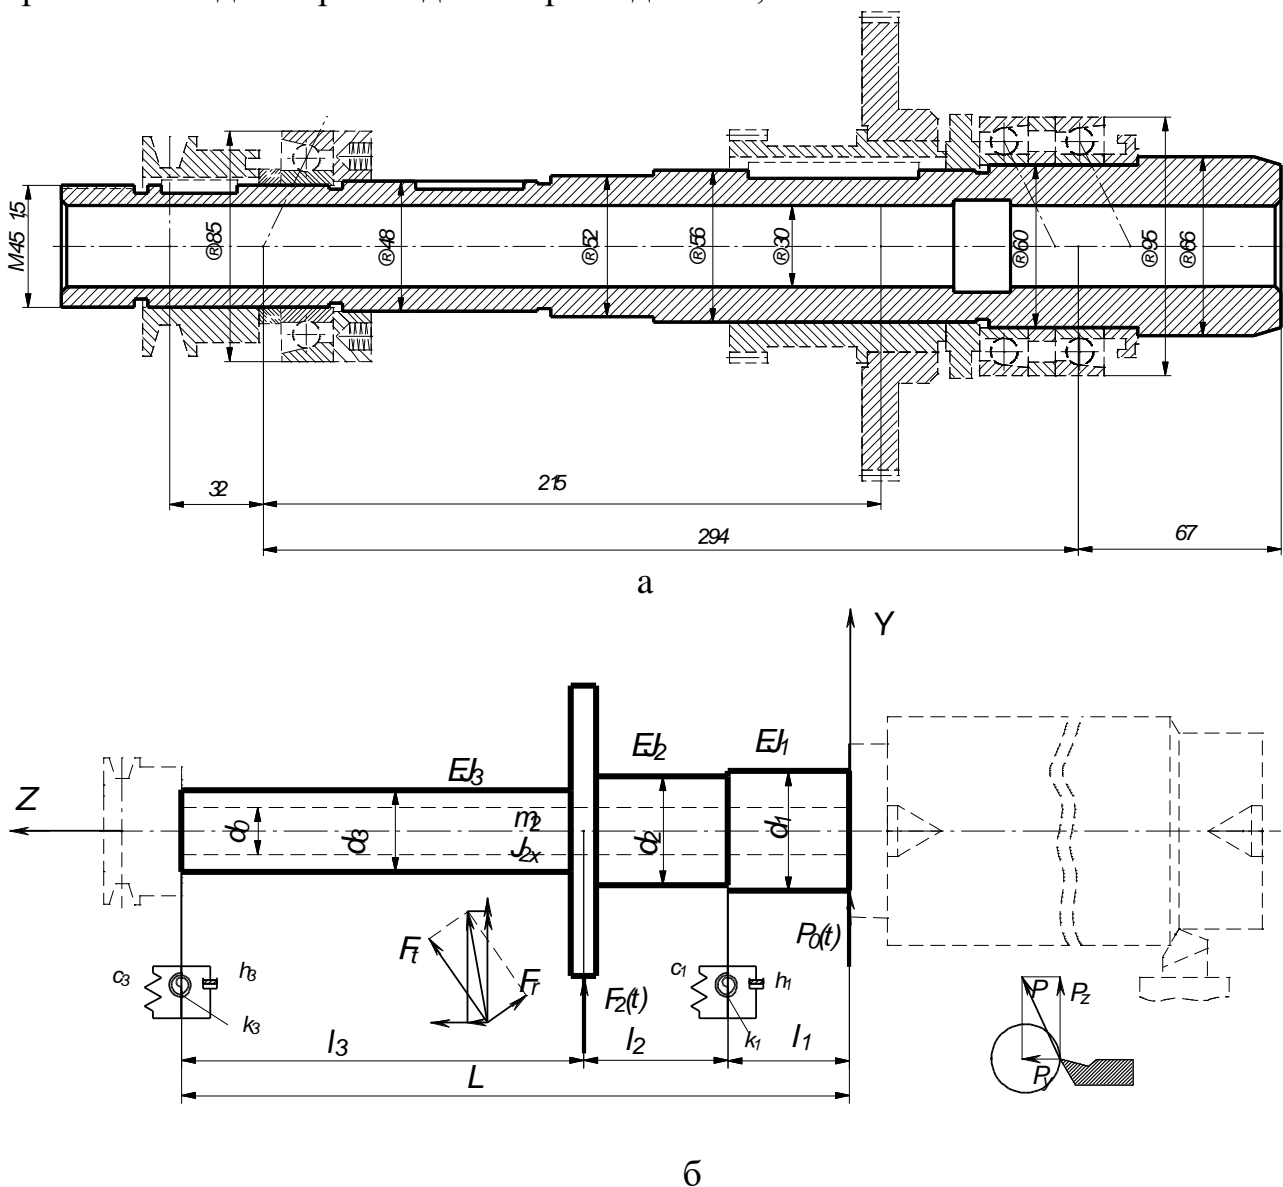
Конструктивна (а) та розрахункова (б) схеми шпindelного вузла
